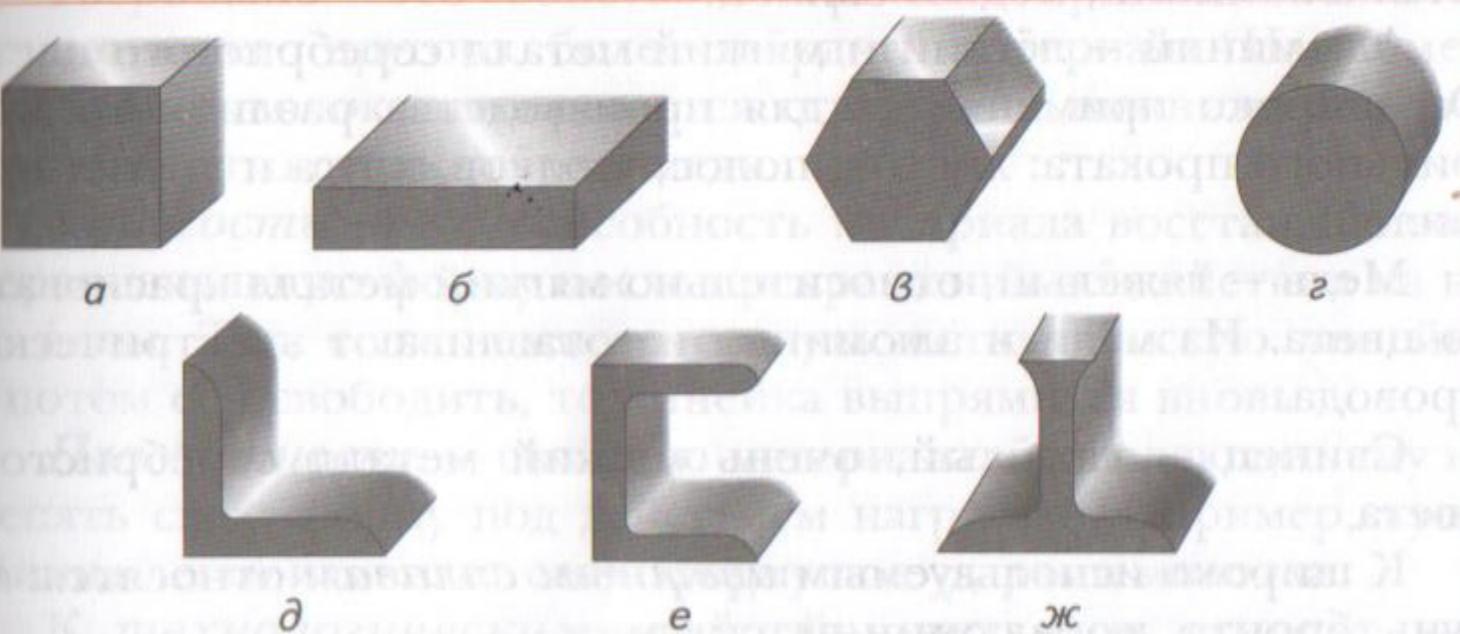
Виды профильного проката металлов: а — квадрат; б — полоса; в — шестиугранник; г — круг; д — уголок; е — швеллер; ж — рельс
